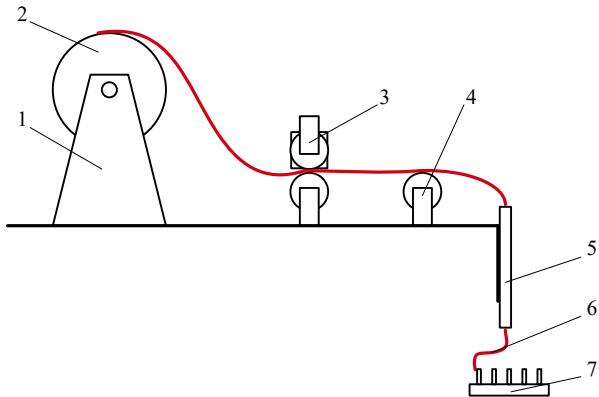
Схема однопниточного нитеукладчика и механизма контроля подачи нити
